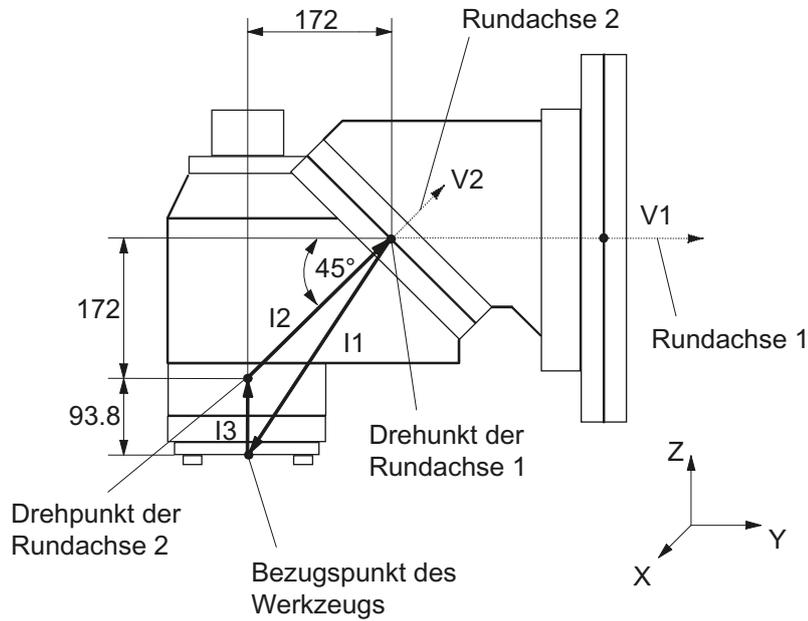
Schwenkkopf 2 "HEAD\_2"
